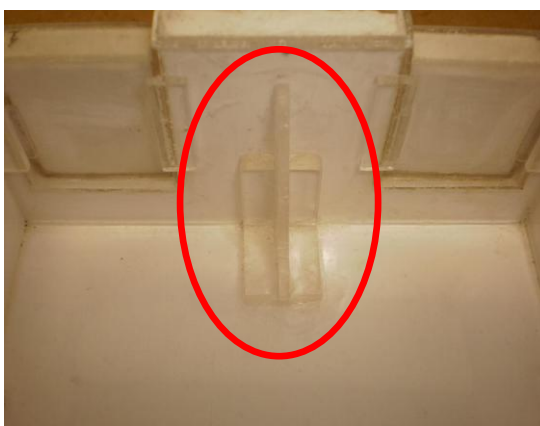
Detalle del blindaje donde se puede observar que los extremos de la caja se encuentran doblados y no soldados (elipse roja).
